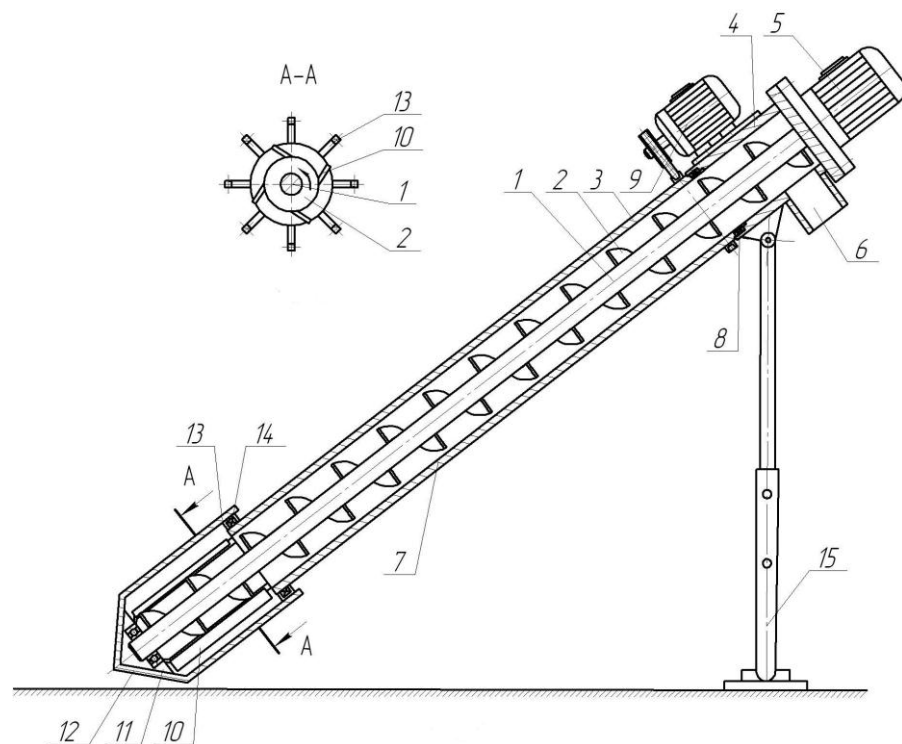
Конструкційна схема гвинтового конвеєра із обертовим кожухом
